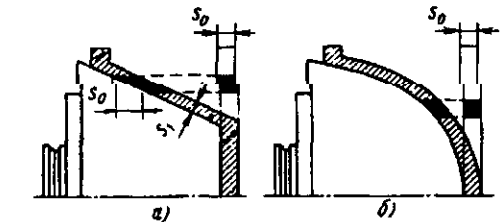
Схемы ротационной вытяжки деталей конической (а) и сложной формы (б) из плоской заготовки
